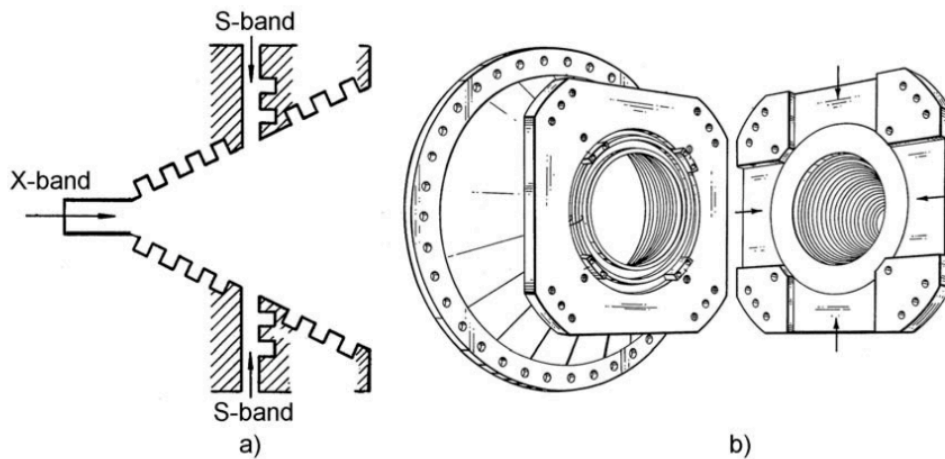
a) Bocina Dual Band con Combinador, b) Corte Trasversal del Combinador
